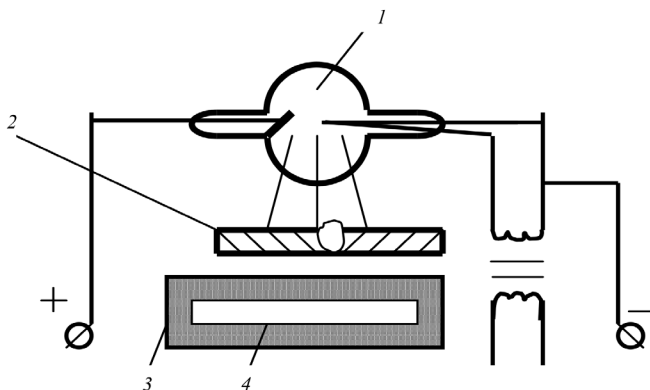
Рентгенографический контроль сварных соединений:
